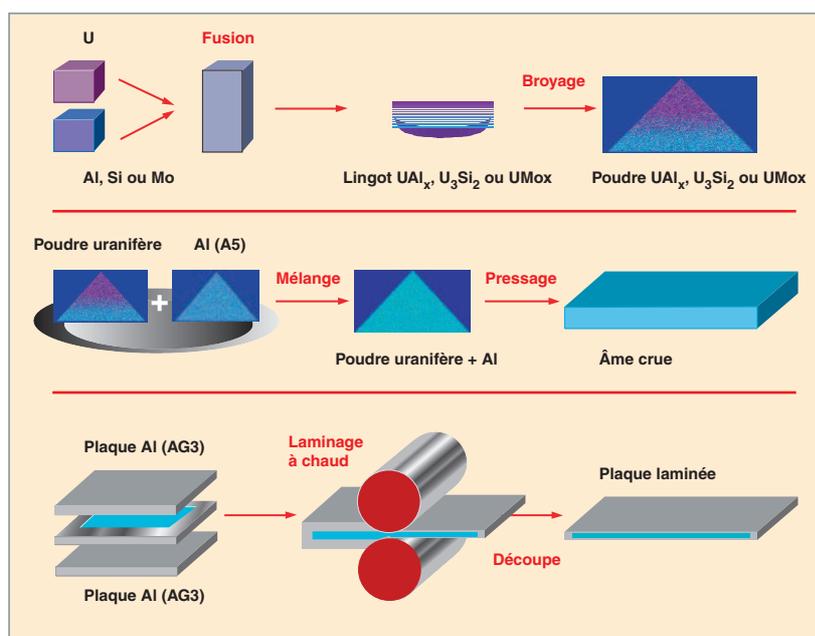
Principe du procédé de fabrication de plaques combustibles par « colaminage ».
